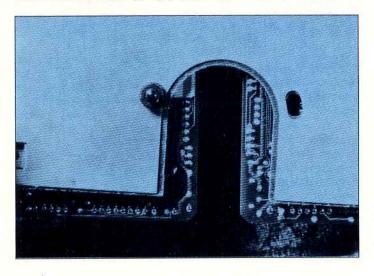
Die Bohrung für den Fototransistor sollte sechs bis acht Millimeter betragen
